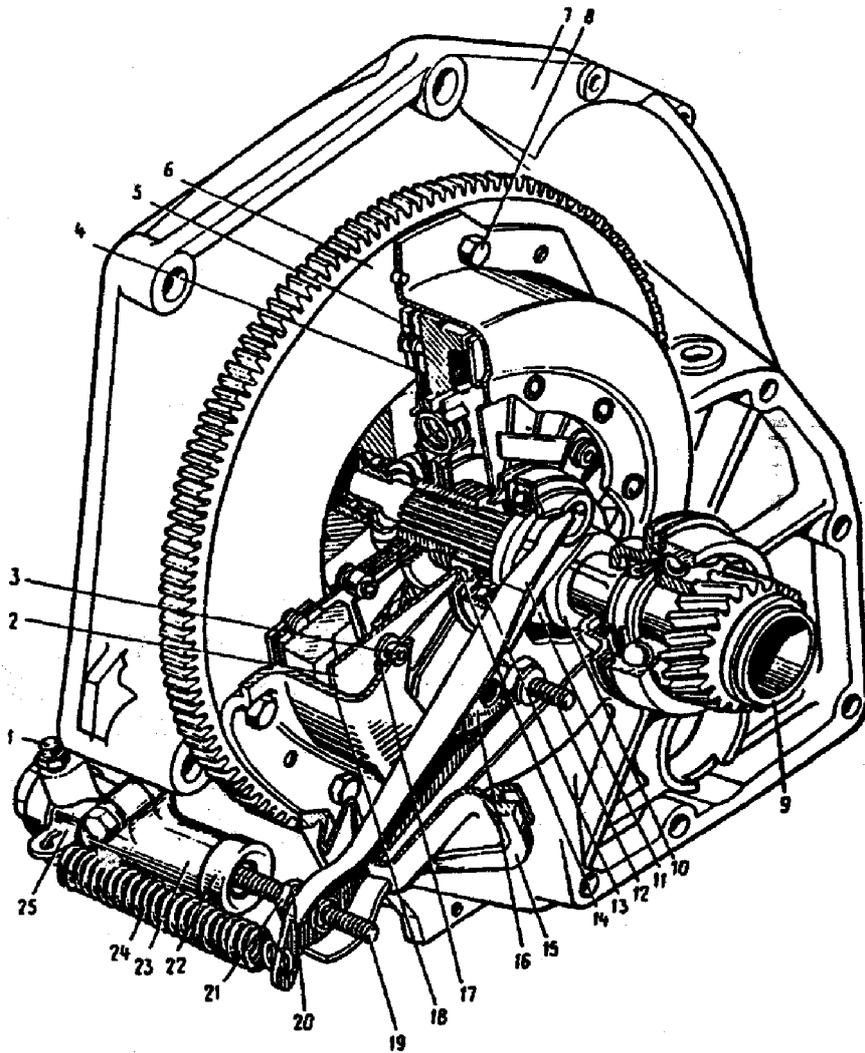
Conjunto da embreagem: 1 - sangrador; 2 - mola diafragma da embreagem; 3 - suporte da mola tipo diafragma; 4 - placa de pressão - platô; 5 - disco da embreagem; 6 - volante; 7 - carcaça da embreagem; 8 - parafuso de fixação do conjunto da embreagem ao volante; 9 - árvore primária da caixa de mudanças; 10 - cubo da embreagem; 11 - garfo da embreagem; 12 - apoio esférico do garfo da embreagem; 13 - rolamento da embreagem; 14 - flange de encosto da mola diafragma; 15 - suporte do garfo da embreagem; 16 - mola do garfo da embreagem; 17 - anel de apoio da mola da embreagem; 18 - carcaça do platô; 19 - haste do garfo da embreagem; 20 - porca de ajuste; 21 - contraporca; 22 - coifa protetora; 23 - cilindro atuador da embreagem; 24 - mola de retorno do garfo; 25 - garra da mola de retorno.
